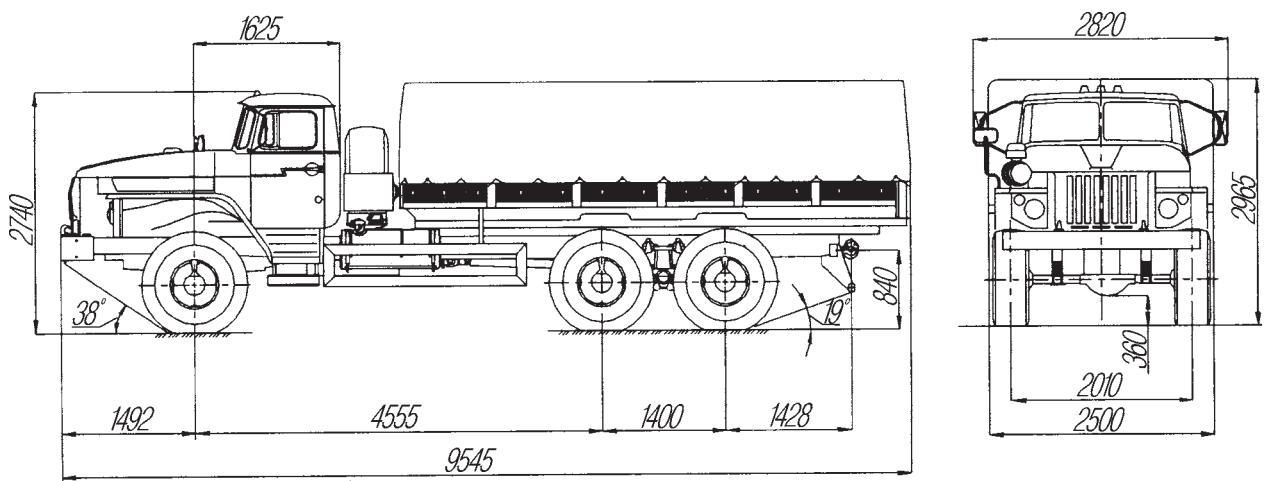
Габаритные размеры автомобиля Урал-4320-0911-30
